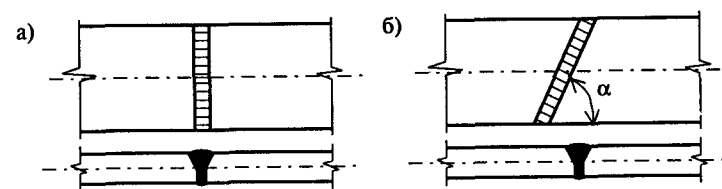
Стыковые сварные соединения: а) прямой стыковой шов; б) косой стыковой шов,  $\alpha = 45-60^\circ$
